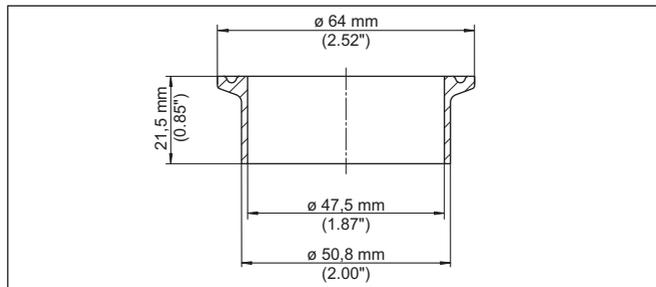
Medidas racor para soldar Clamp 2" (DIN 32676, ISO 2852) PN 16
